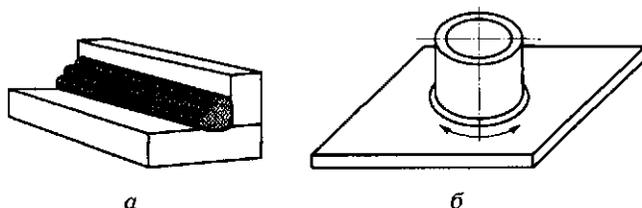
Положение при сварке тавровых швов:
